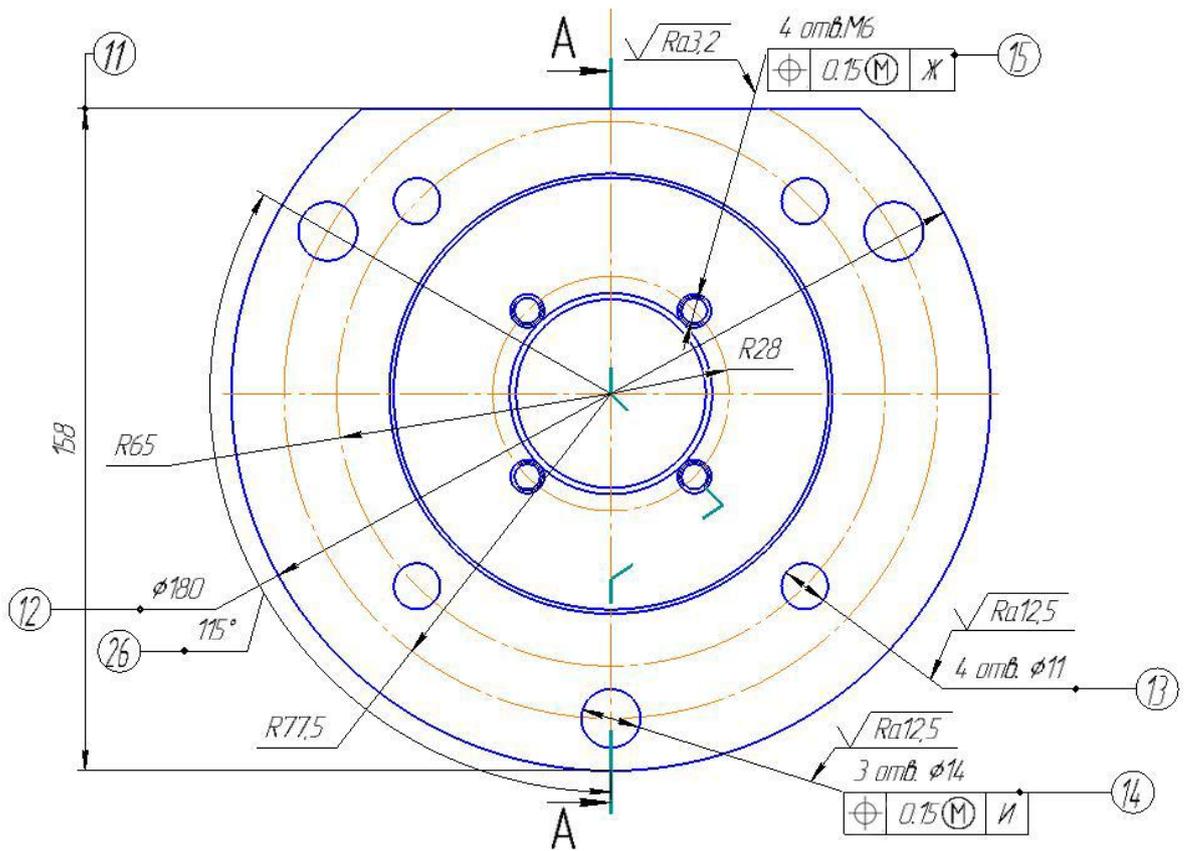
Главный вид по чертежу. Нумерование поверхностей детали
